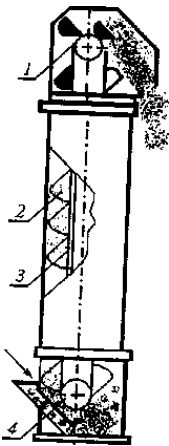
Схемы нории с центробежной разгрузкой: 1 -приводные звездочки- 2 - ковши 3 - тяговые органы; 4 - натяжная звездочка
